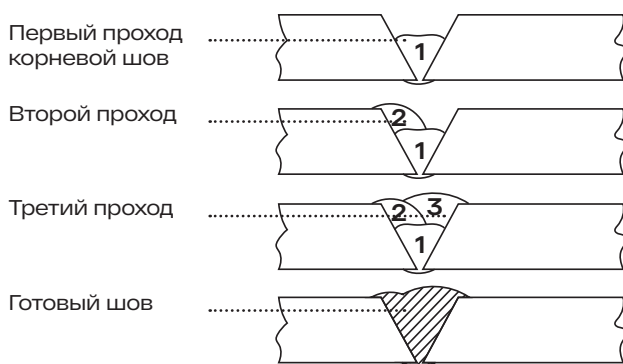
Многопроходная сварка стыковых соединений
